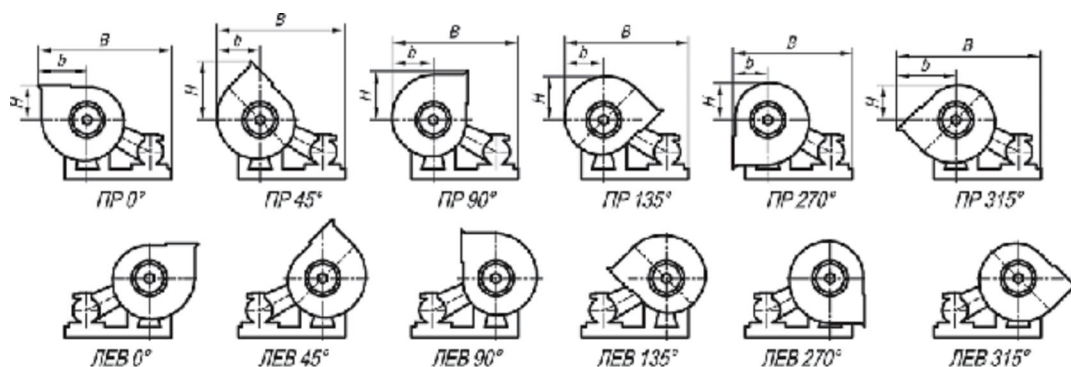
Положения корпуса вентилятора ВР 1320-30 исп-5.
